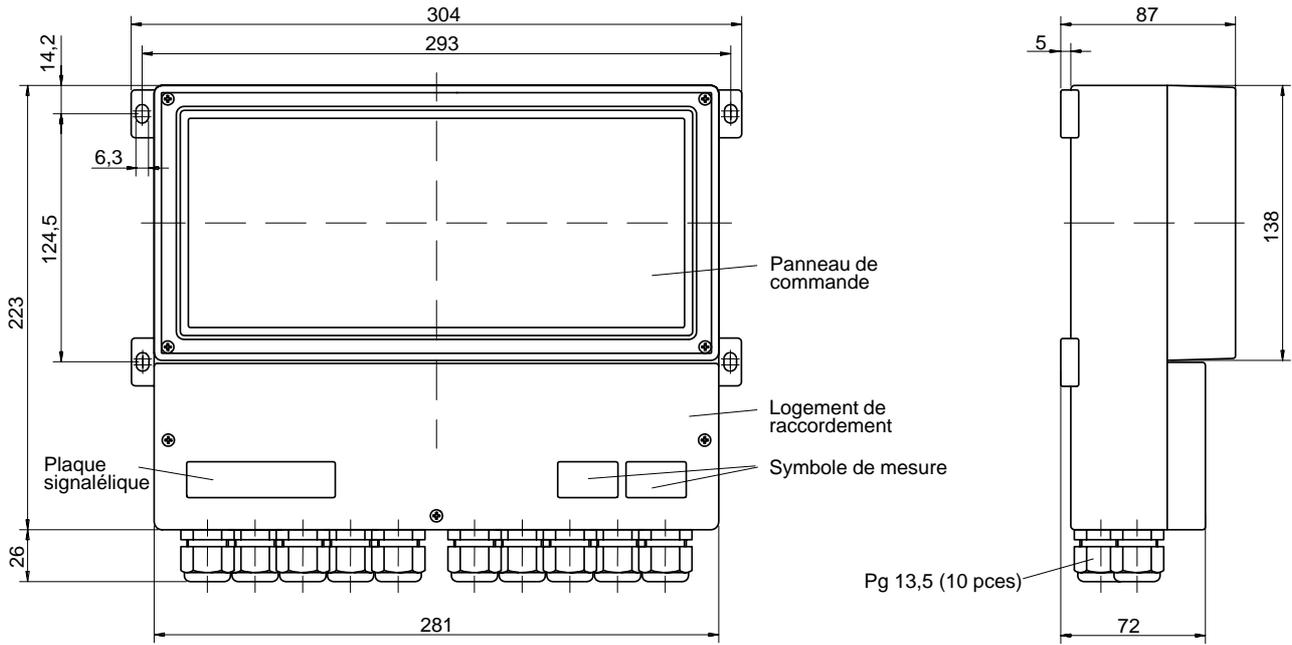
Dessin d'encombrement du Transmetteur O₂ 4500
